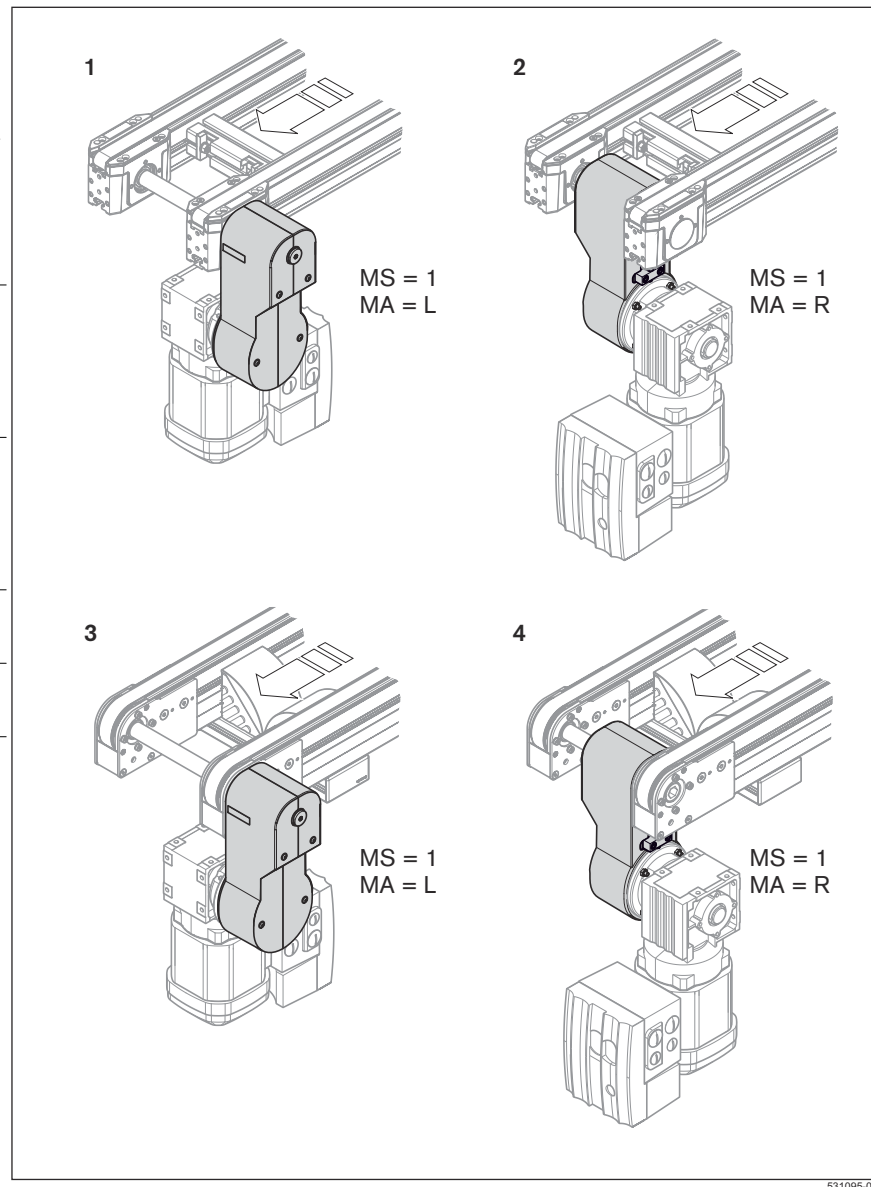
Posiciones de montaje posibles en el tramo de cinta, ejemplos CSS/...
